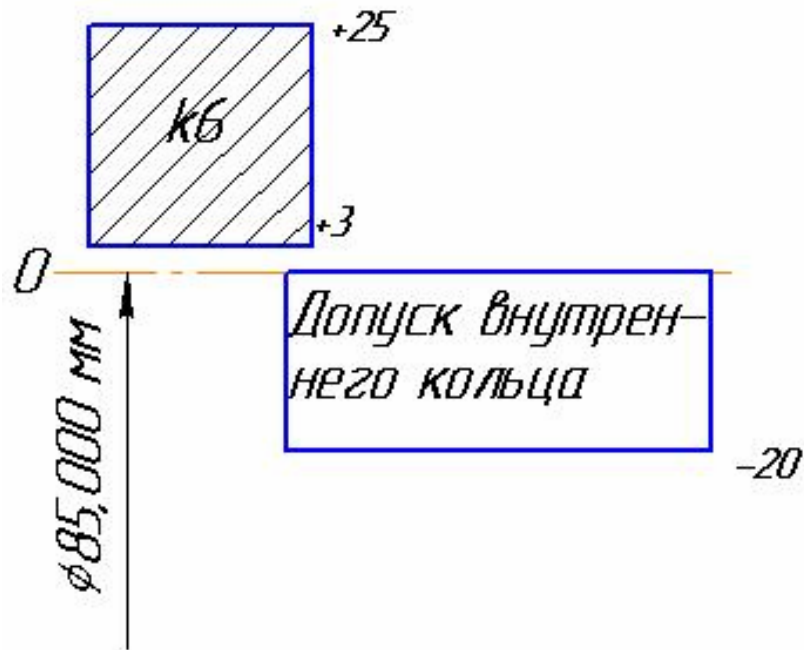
Схема поля допуска посадки внутреннего кольца с валом
